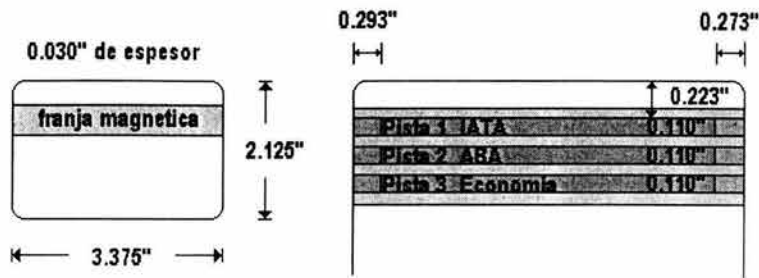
Tarjetas magnéticas: dimensiones y formatos.
